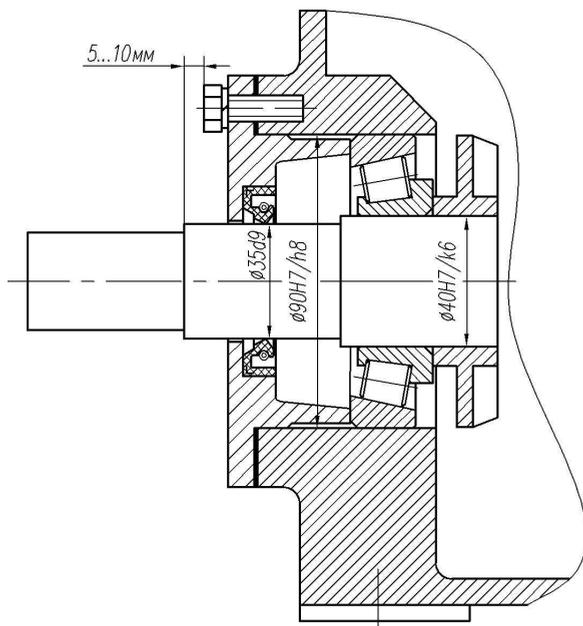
Установка крышки подшипникового узла и разбрызгивателя на быстрходном валу редуктора
